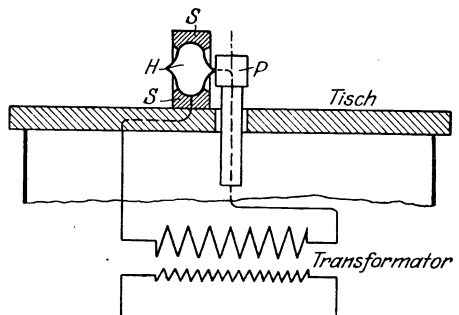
Schema der Hohlkörper-Nahtschweißung.
